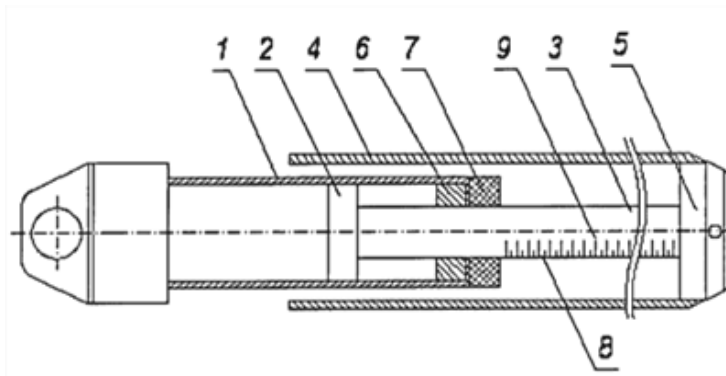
Пристрій для контролю положення штока пневмоциліндра
